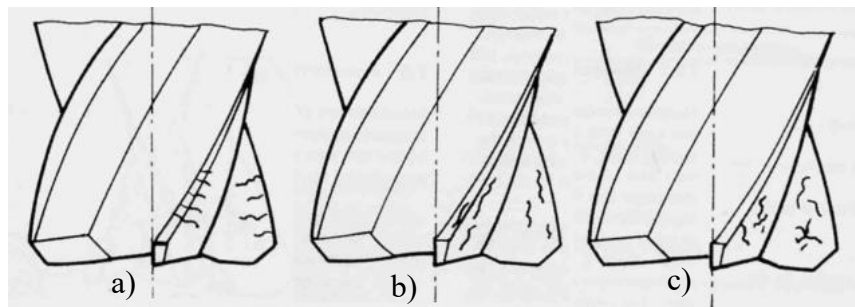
Diferentes Tipos de fissuras em fresas de topo, a) Fissuras Perpendiculares, b) Fissuras Paralelas, c) Fissuras Irregulares (ISO 8688-2, 1989)
